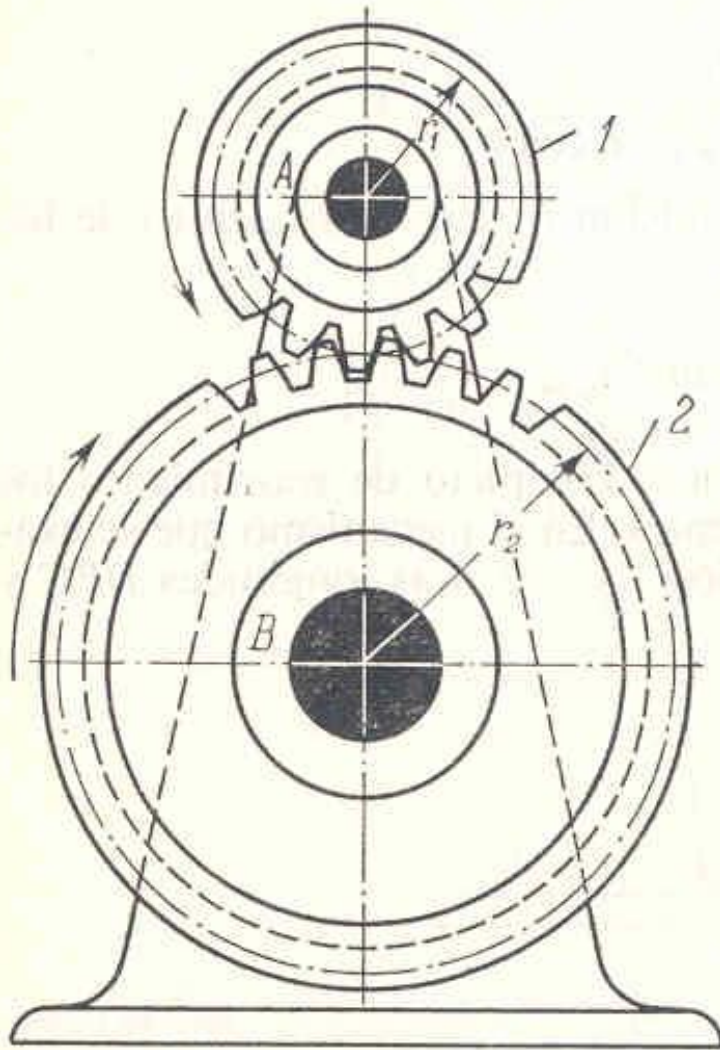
Transmisión del movimiento de rotación por engranajes.
